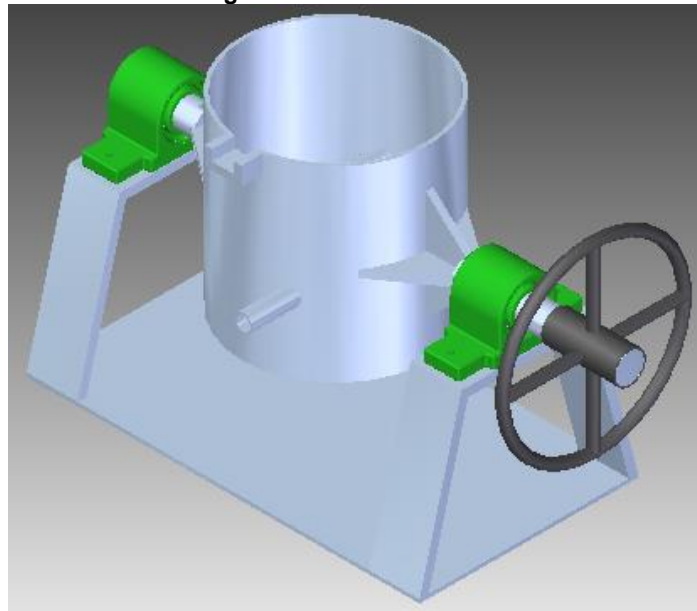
CAD Conjunto Estructura soporte. Fuente: Autor
